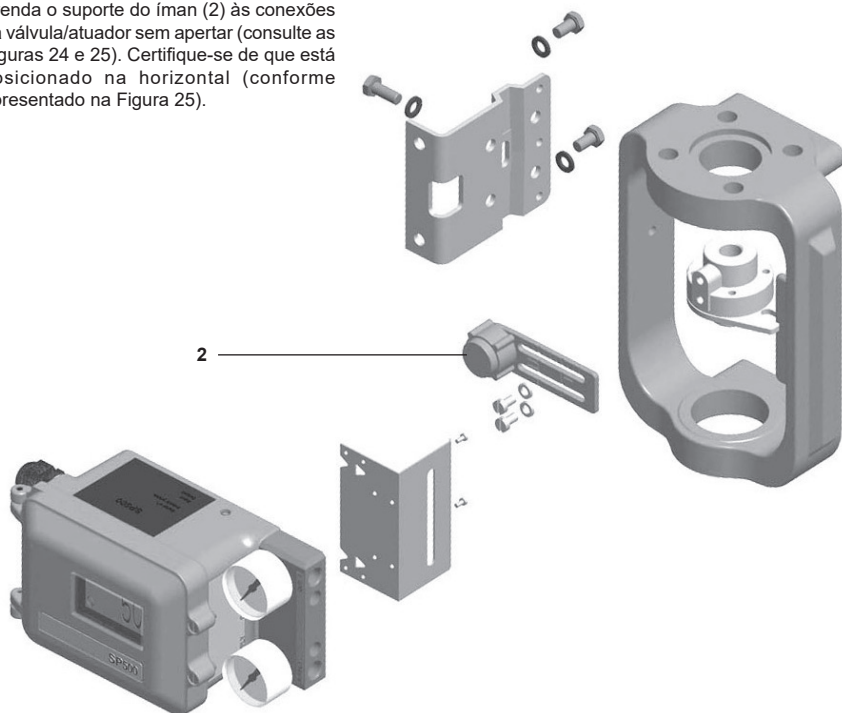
Conjunto de montagem “yoke” para um atuador linear
